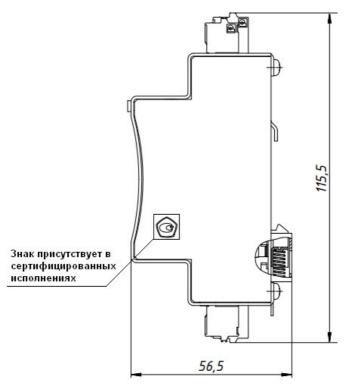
Модуль Элсима-DA01. Габаритно-установочный чертеж. Вид сбоку
